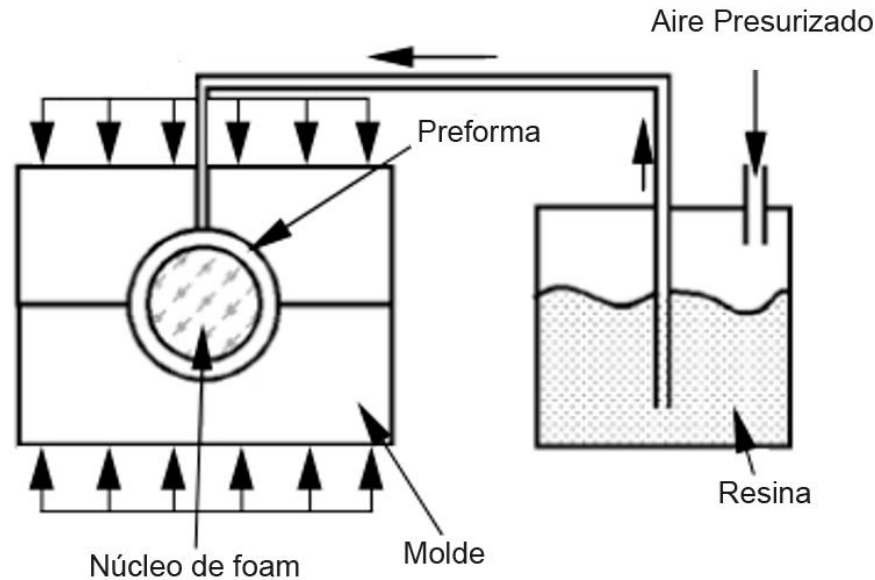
Esquema del proceso de moldeo por inyección de resina. [11]
